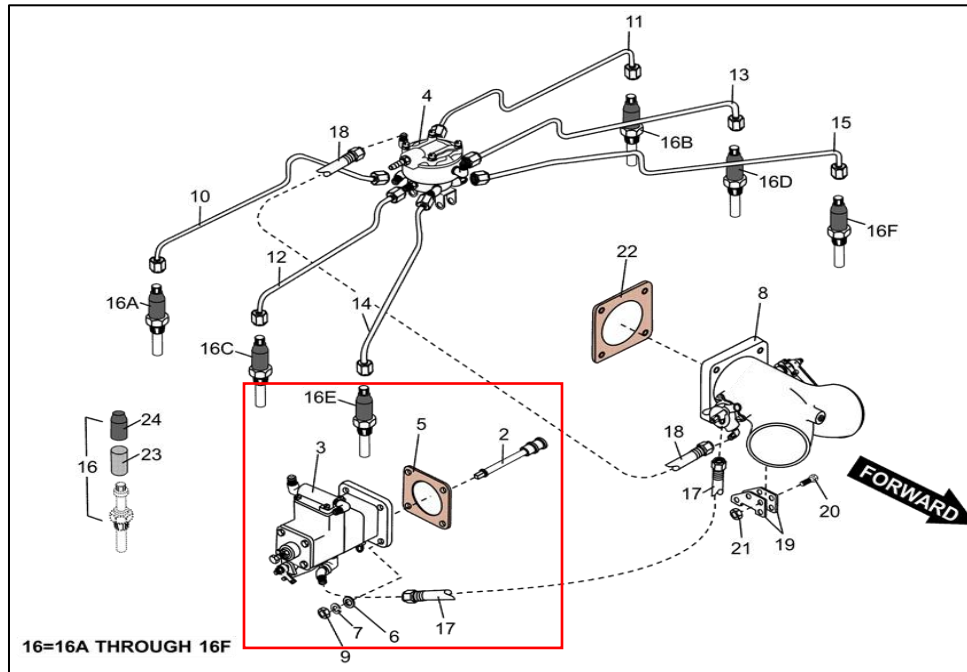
Sistema de inyección de combustible Motor Continental (IO-360K) y bomba de combustible
